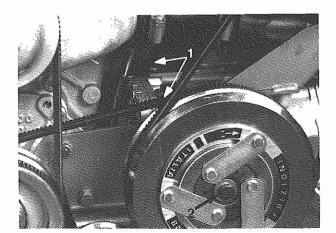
1) Viti fissaggio compressore - Compressor screws 2) Viti fissaggio puleggia - Pulley screws
